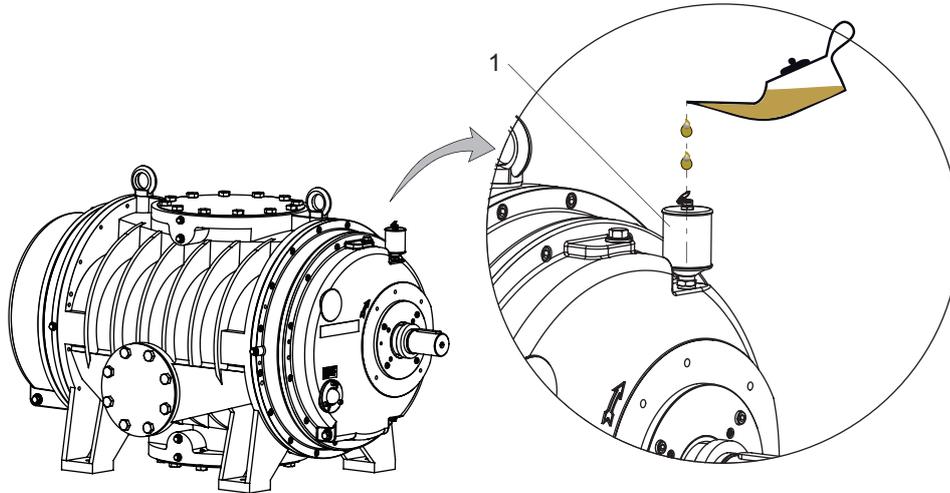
Sperröl für Radialwellendichtringe einfüllen
